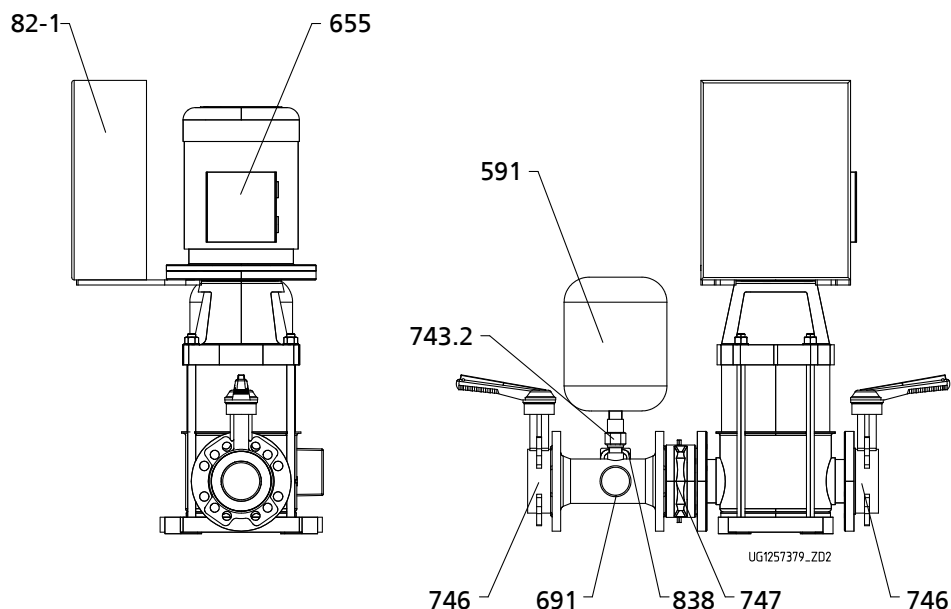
Сборочный чертеж Нya-Solo D с Movitec 25, 40, 60, 90
